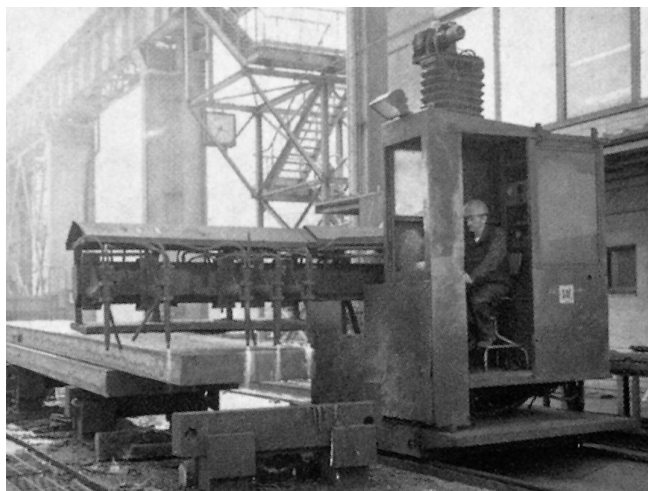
Machine spécifique destinée à prélever par oxycoupage des échantillons de matières [Doc. SAF]
